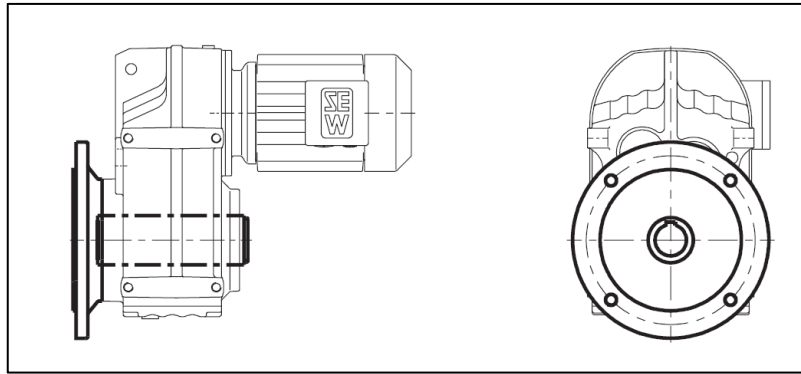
Representação de um motoredutor de eixos paralelos de eixo ocado
